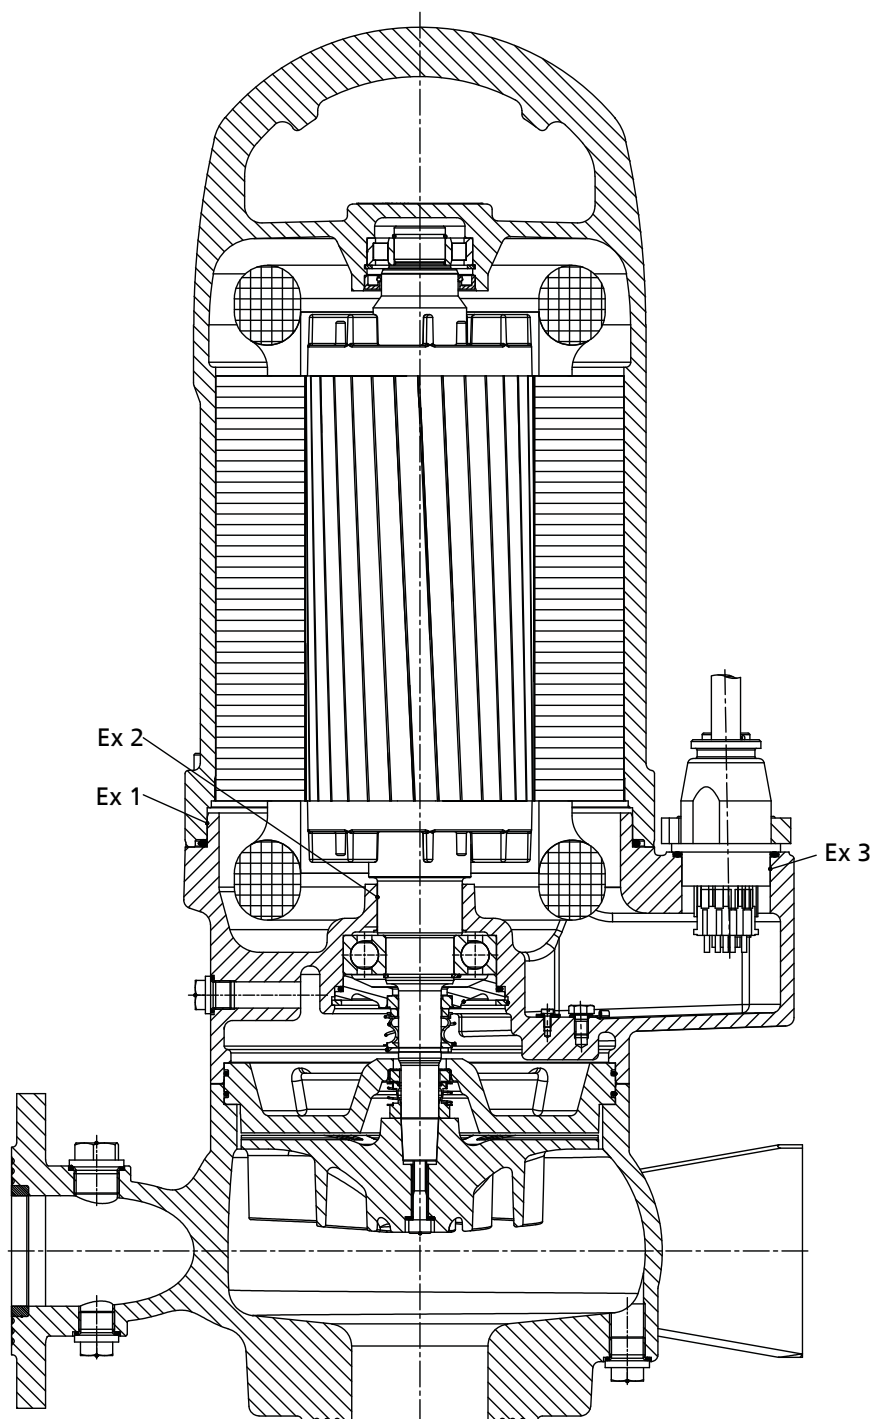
Plochy mezer chráněné proti výbuchu Amarex KRT, typ motoru 1
